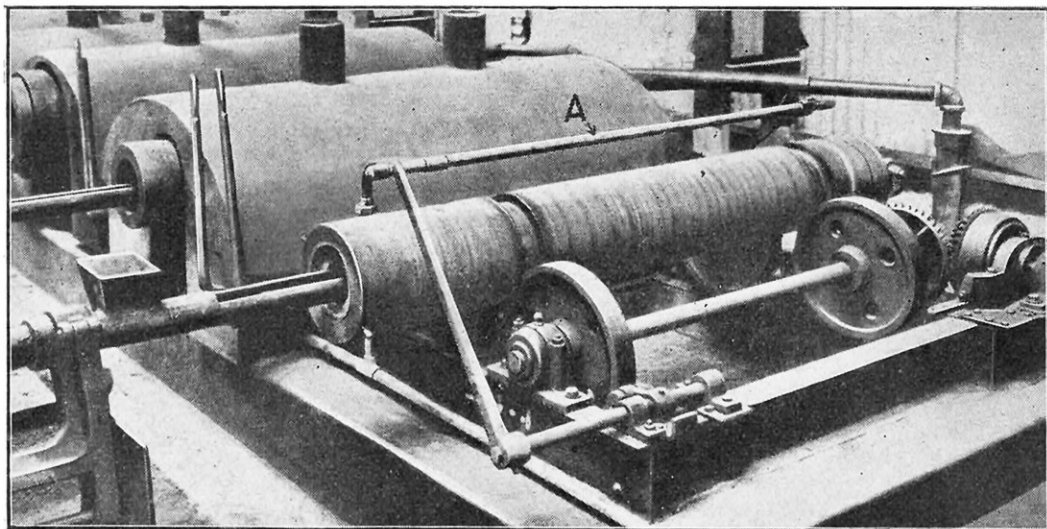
MACHINE BRÉSILIENNE PRIMITIVE POUR EXÉCUTER LA COULÉE ROTATIVE
